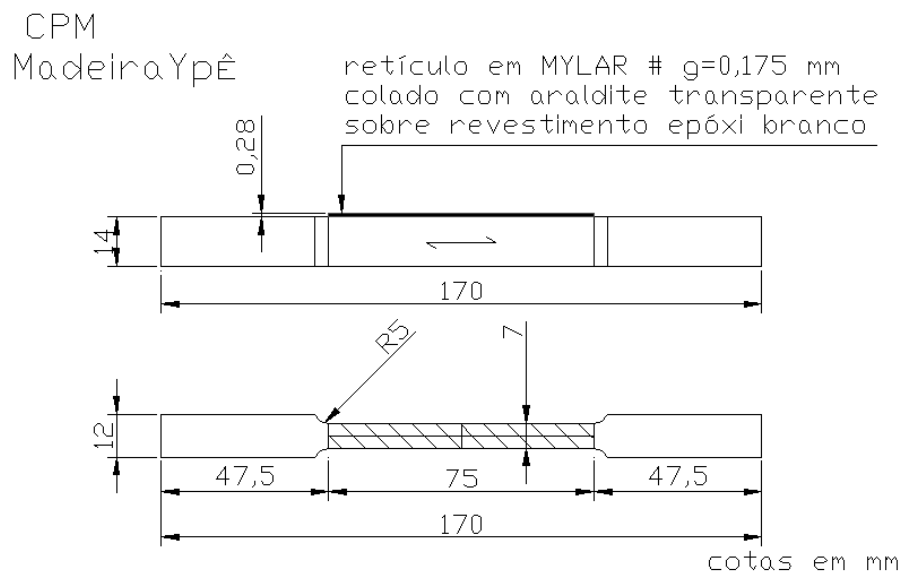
Detalhes do CPM para ensaio de tração.
